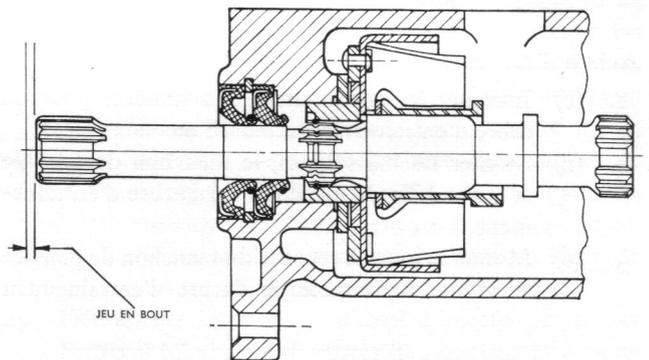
Vue d'un arbre d'entraînement d'une seule pièce illustrant le jeu en bout
